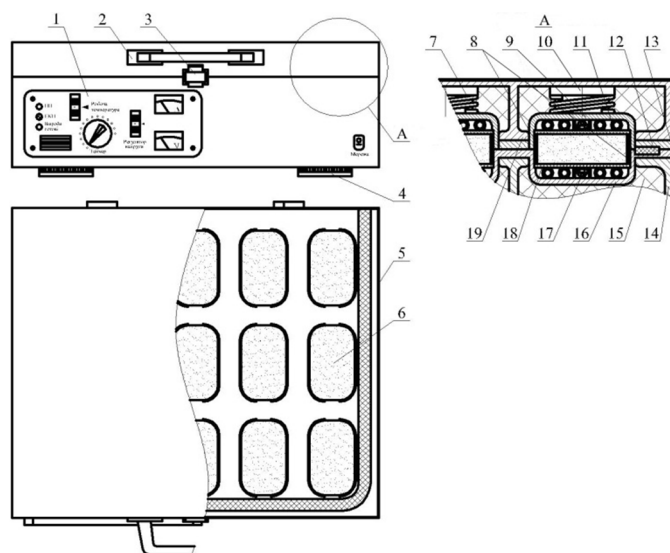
Пристрій ПКС-0,18: 1 — пульт керування; 2 — ручка; 3 — механічний затискувач; 4 — опорні ніжки; 5 — облицювальні сталеві листи; 6 — напівфабрикати; 7 — пружини; 8 — різнополярні електроди; 9 — рухомі утримувачі; 10 — фіксатори; 11 — електронагрівачі; 12 — прокладка з термостійкої гуми; 13 — плита з отворами; 14, 19 — нижній і верхній каркас; 15 — теплоізоляція; 16 — штампована основа; 17 — термодатчики; 18 — гріючі плитки
